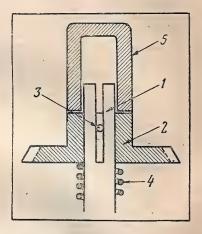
Механизм расцепления шестерен: 1— вал, $\sqrt{2}$ — ведущая шестерня, 3— шпилька, 4— пружинка, 5— нажимной колпак
